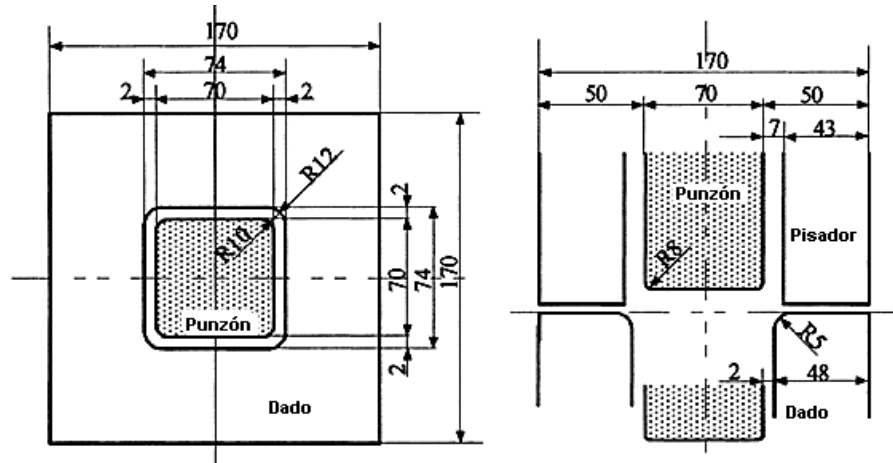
Dimensiones de las herramientas para el embutido cuadrado (mm) [54].
